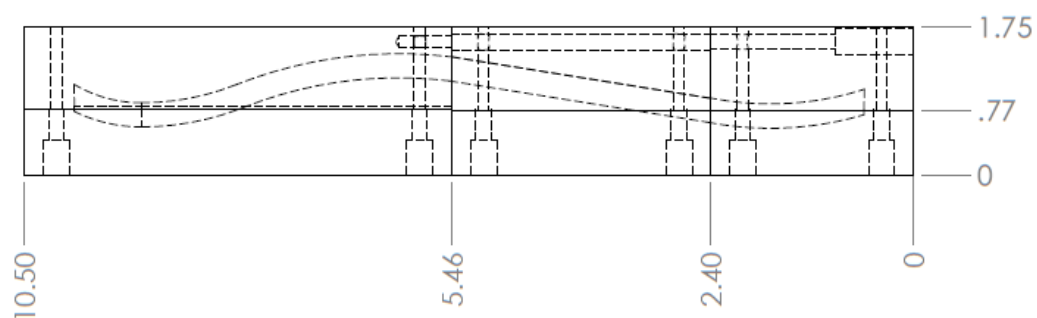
Dibujo de molde inferior con dimensiones y componentes Rev. 3
